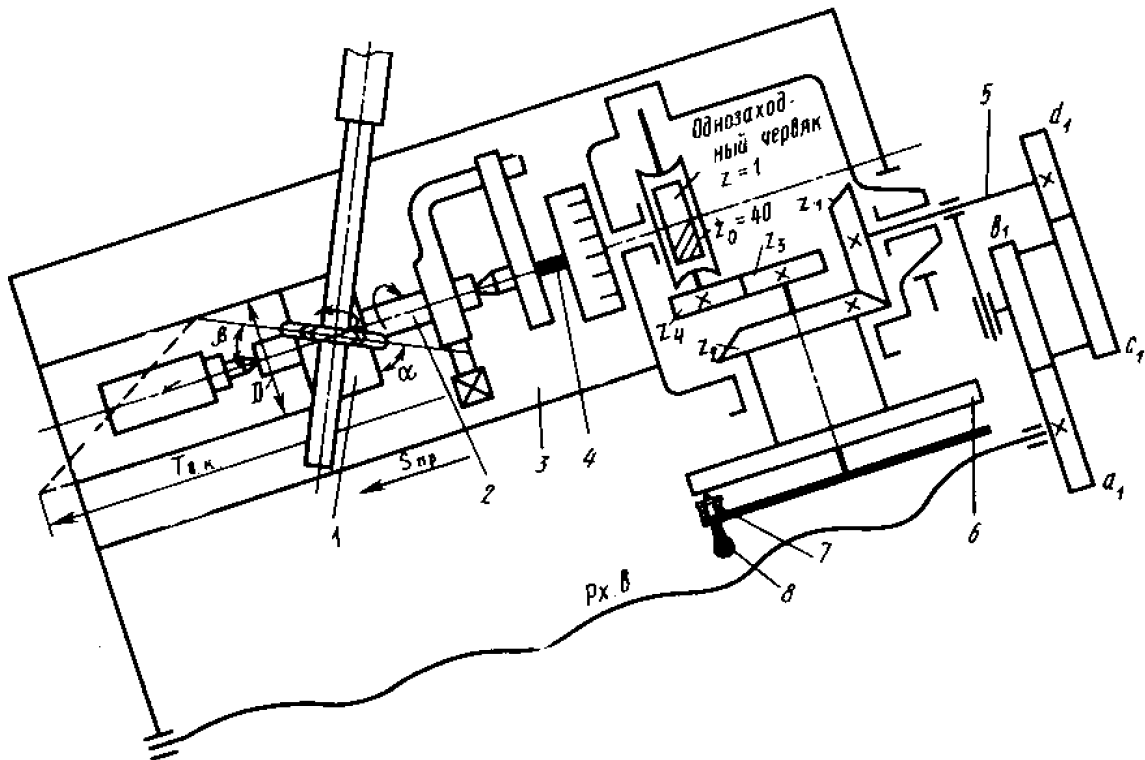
Схема наладки универсально-фрезерного станка и делительной головки на фрезерование винтовых канавок:
